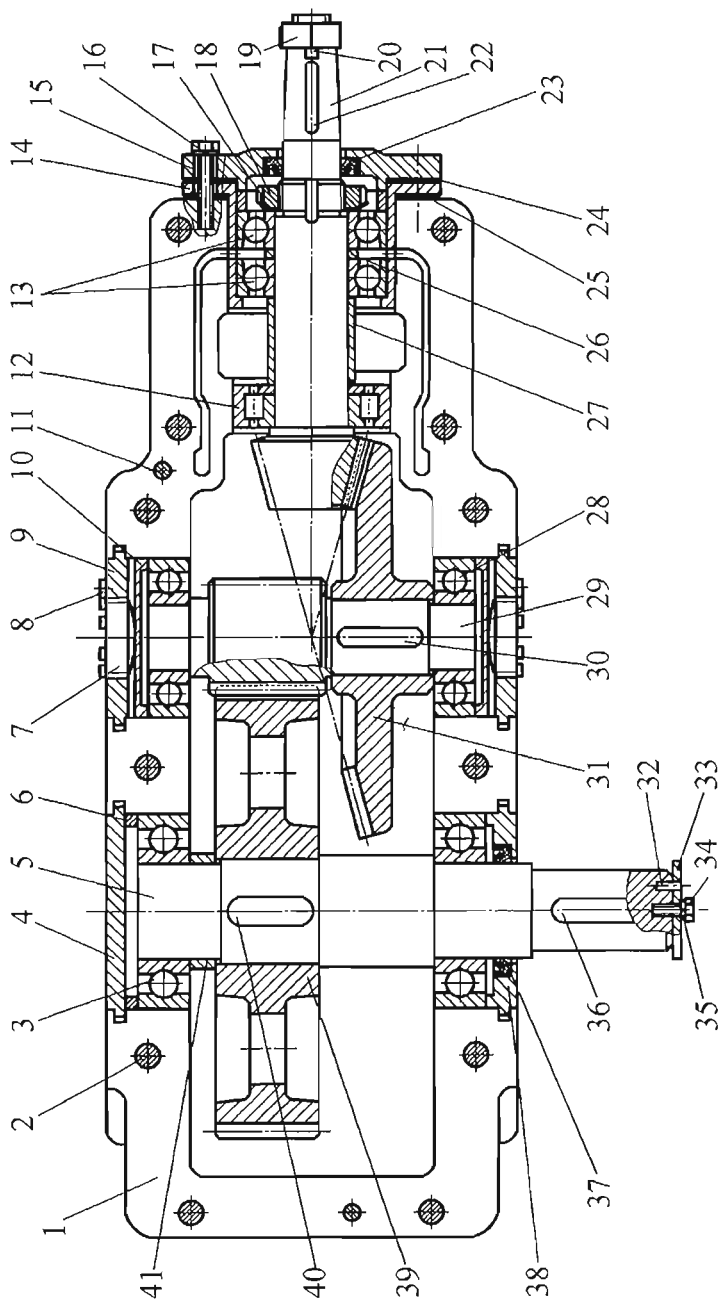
Конструкция двухступенчатого коническо-цилиндрического редуктора
